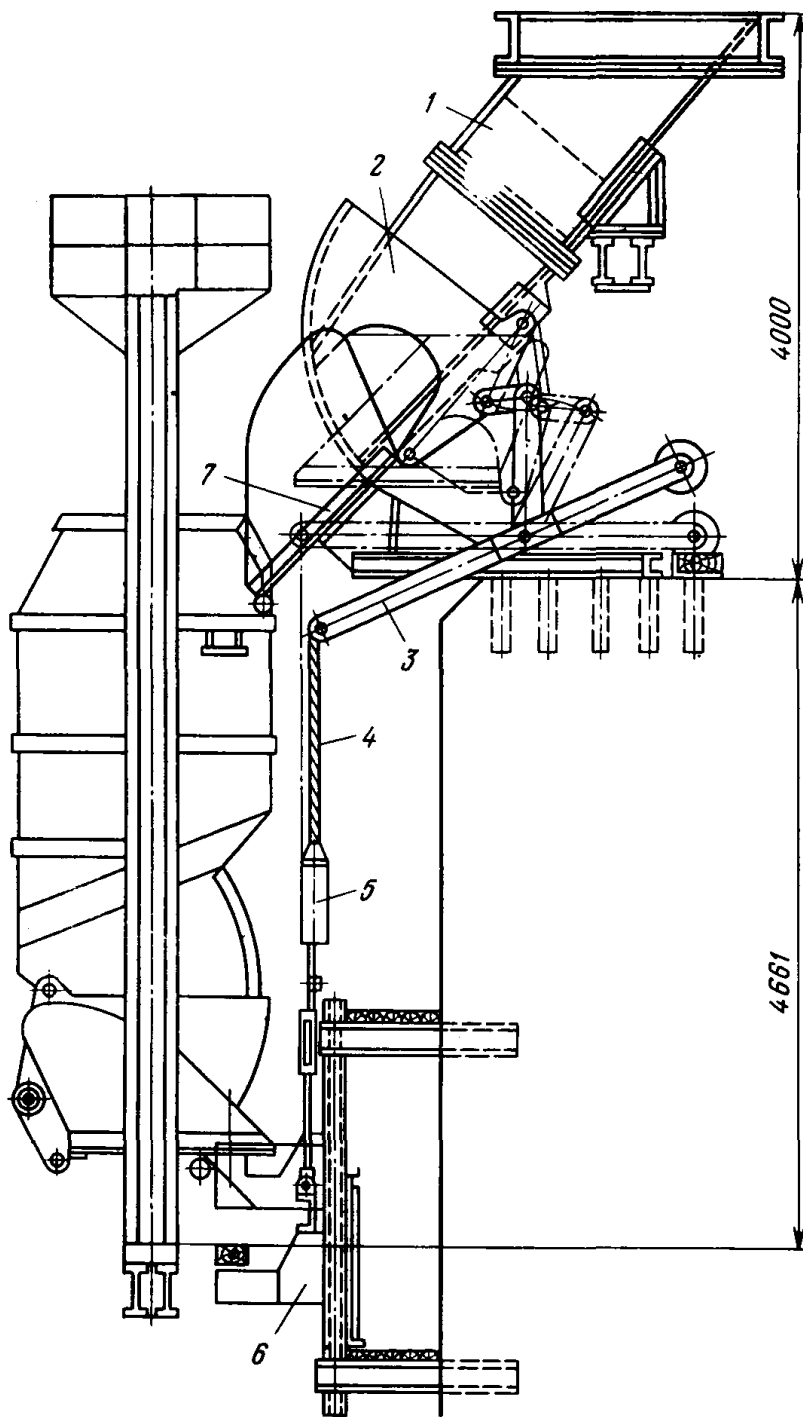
Загрузочное устройство с секторным затвором с дозировкой скипа ваго-
